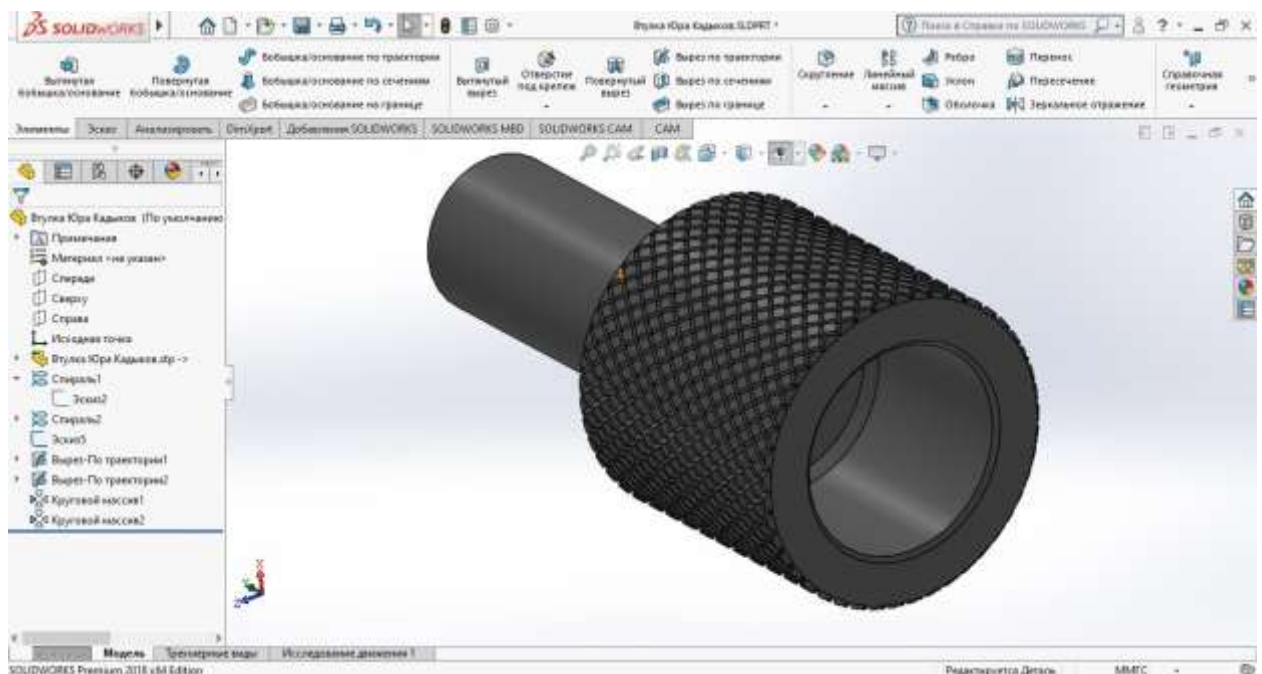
3-D модель деталі «Втулка рифлена» (Вид 2)
